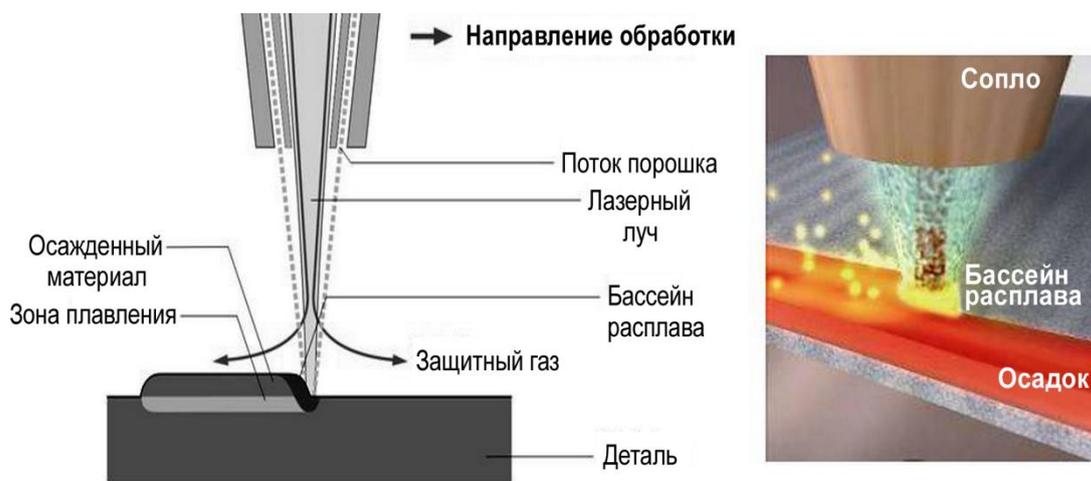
Схема процесса лазерной наплавки (с подачей материала)
